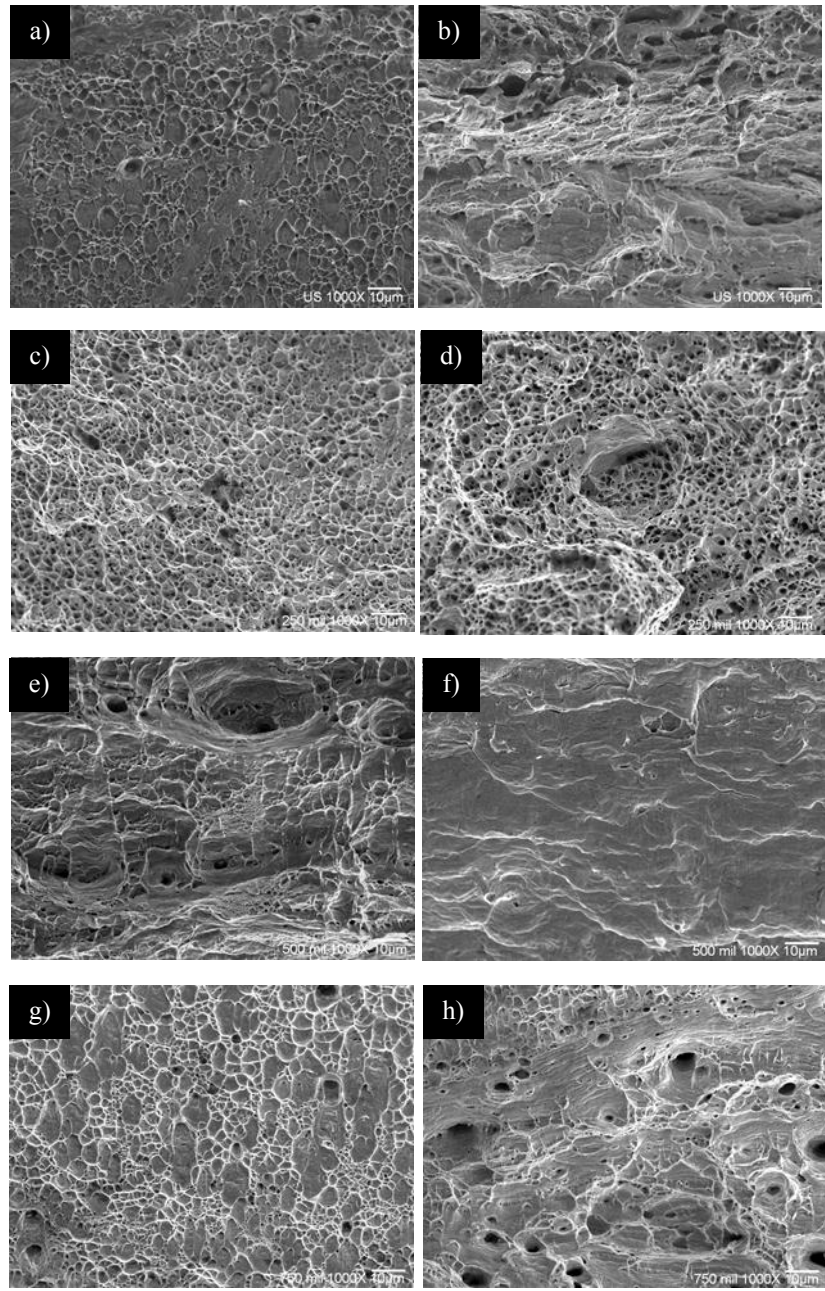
Fractografías de a) ensayo de tensión de unión soldada R1, b) unión soldada R2, c) unión soldada con 25% de daño R1, d) unión soldada con 25% de daño R2, e) unión soldada con 50% de daño R1, f) unión soldada con 50% de daño R2, g) unión soldada con 75% de daño R1 y h) unión soldada con 75% de daño R2.
